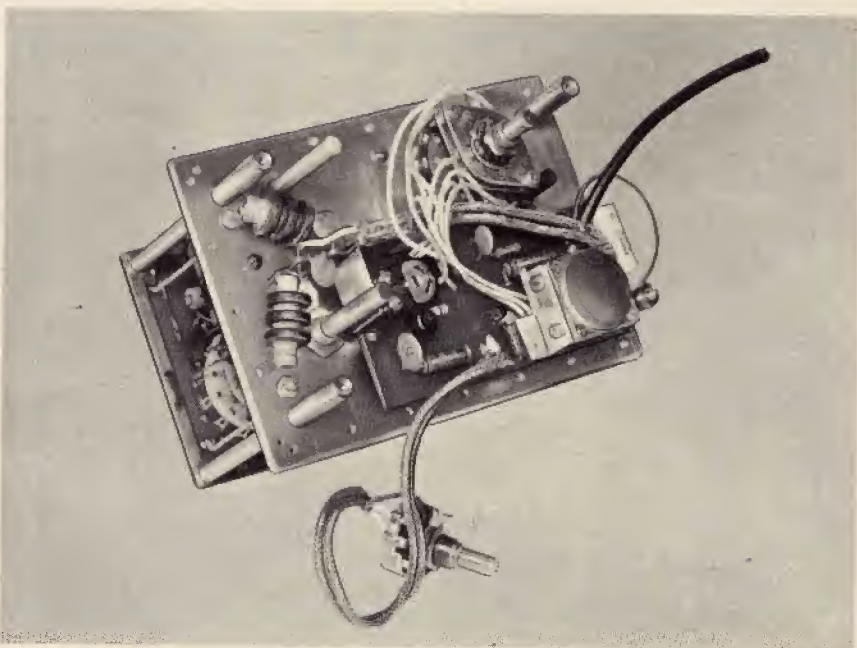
Vista di insieme del generatore di BF - modulatore montato sui due supporti - distanziatori e disposto tra i comandi del pannello frontale della scatola schermo del generatore.
